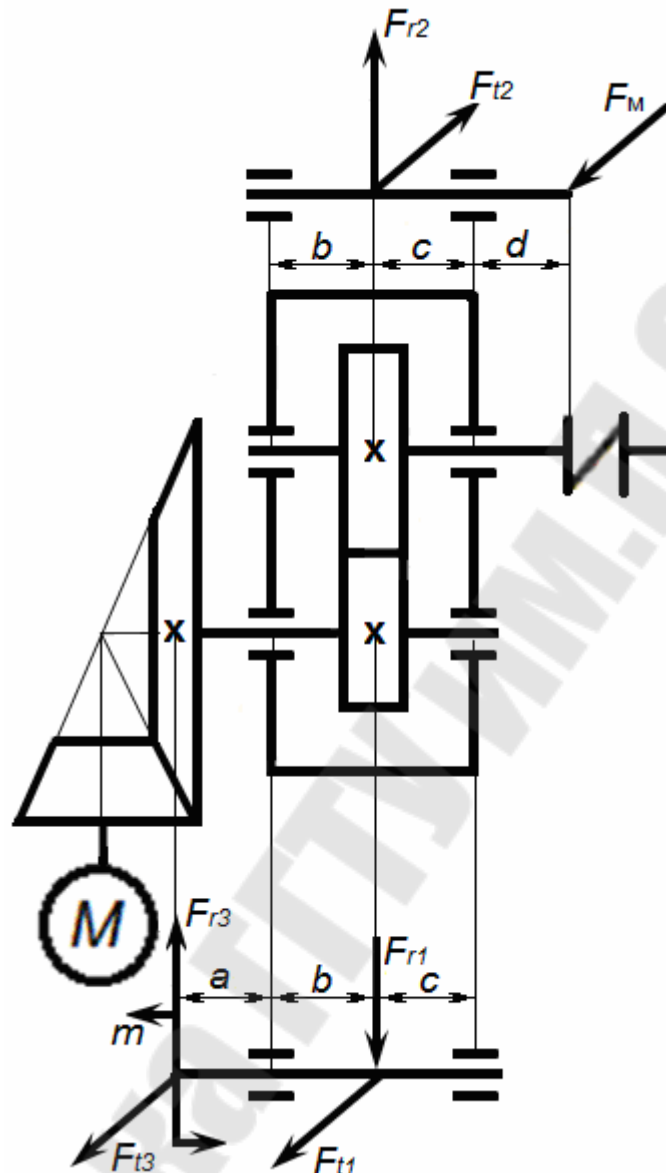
Привод конвейера с открытой конической зубчатой передачей
